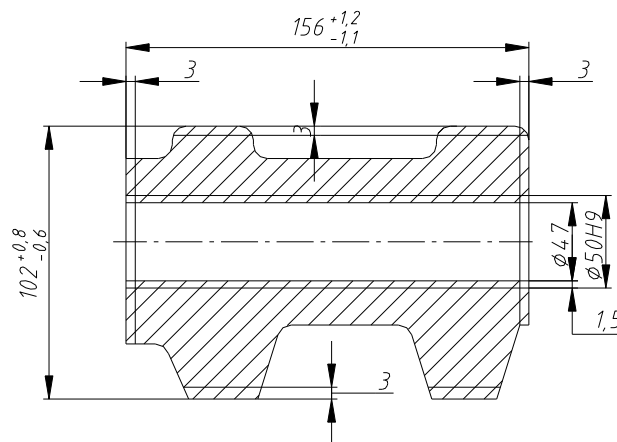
Заготовка корпуса з нарахованими припусками і допусками.
